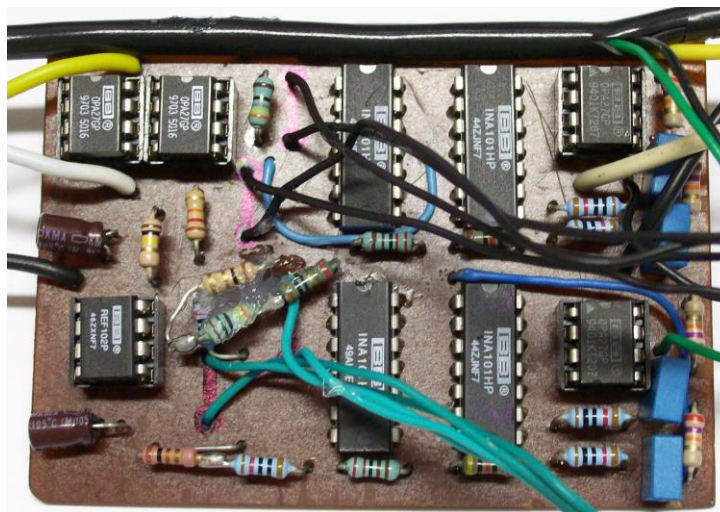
Placa de circuito impresso do condicionador de sinais projetado. Cada placa possui dois condicionadores.
